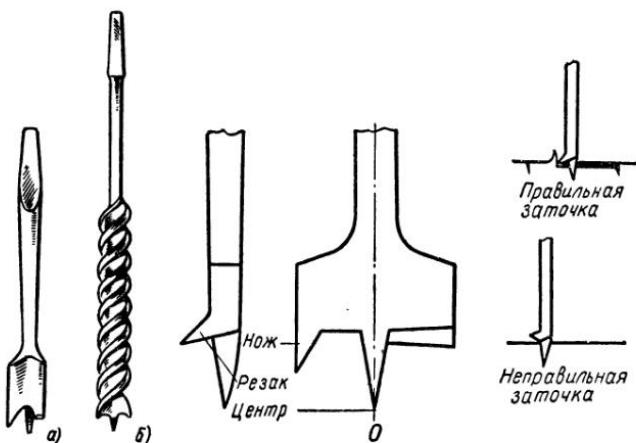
Сверла: а — первое (перка); б — винтовое.
